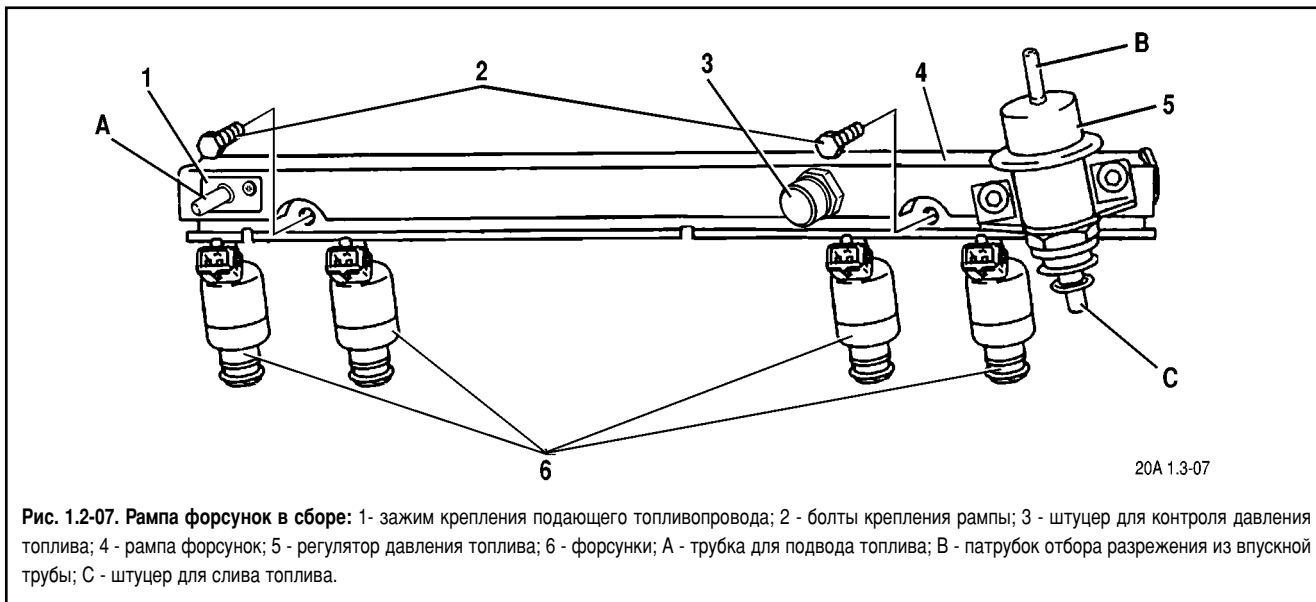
Рампа форсунок в сборе: 1 - зажим крепления подающего топливопровода; 2 - болты крепления рамп; 3 - штуцер для контроля давления топлива; 4 - рампа форсунок; 5 - регулятор давления топлива; 6 - форсунки; А - трубка для подвода топлива; В - патрубок отбора разрежения из впускной трубы; С - штуцер для слива топлива.
